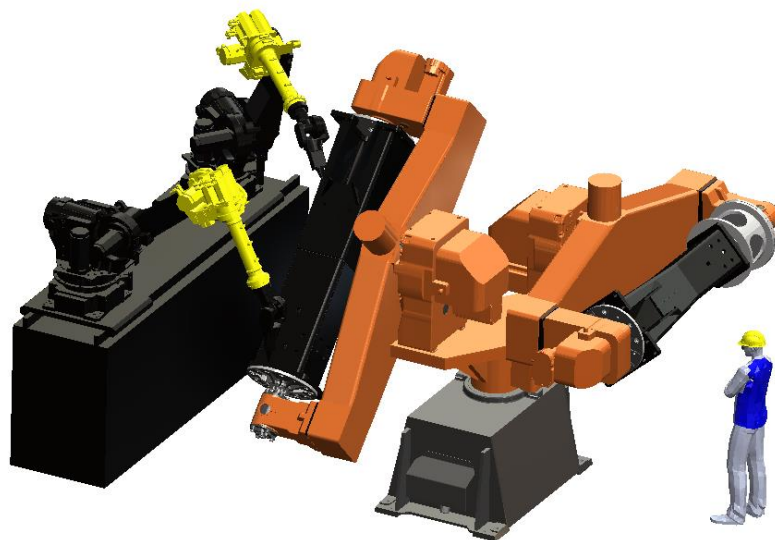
Приклад роботизованого зварювання (використання обертально – поворотного пристрою зі зварювальними роботами)
